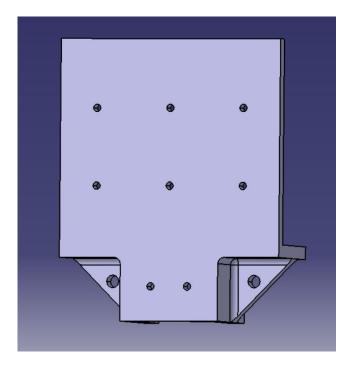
Conector ajustable de acero galvanizado Fuente: elaboración propia
